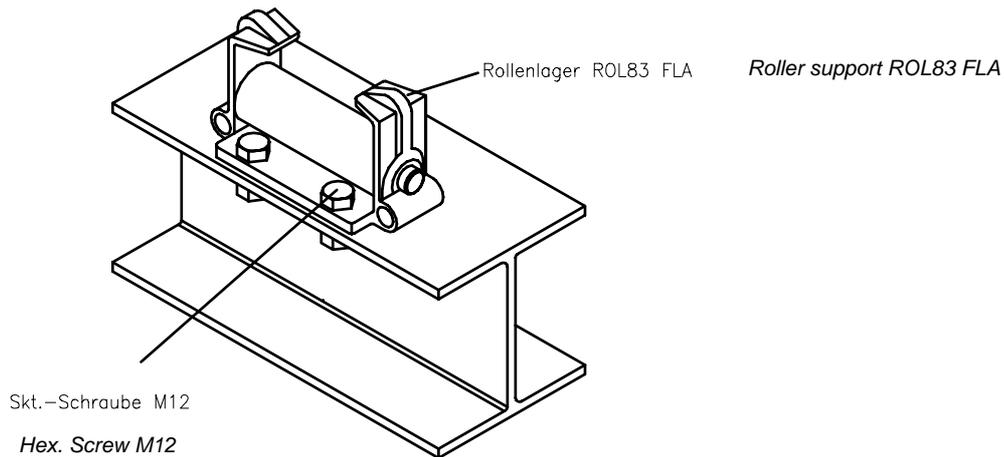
Rollenlager ROL83 für Schraubmontage
